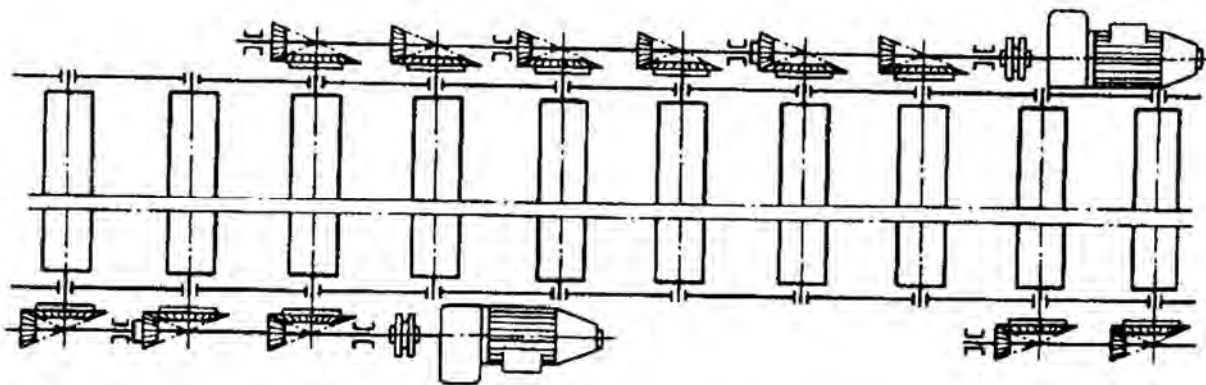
Схема привода роликового конвейера с продольным валом и коническими зубчатыми передачами
